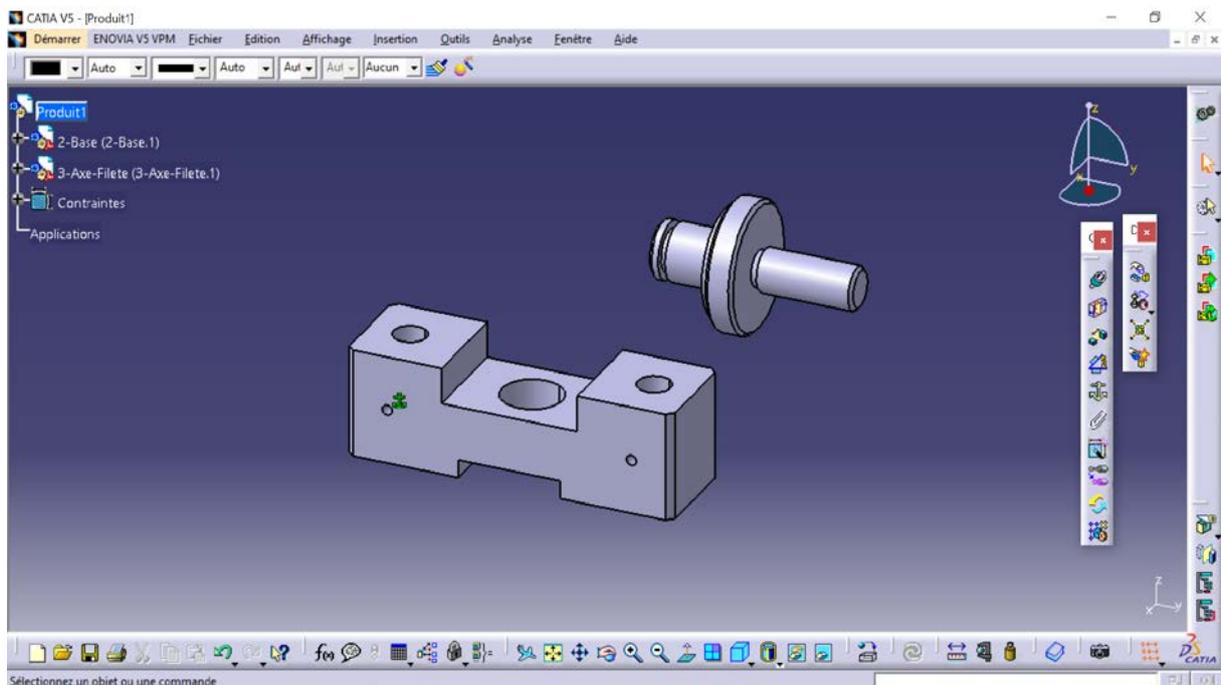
Assembly Design (Insertion de l'Axe fileté 3) [1], [2]
